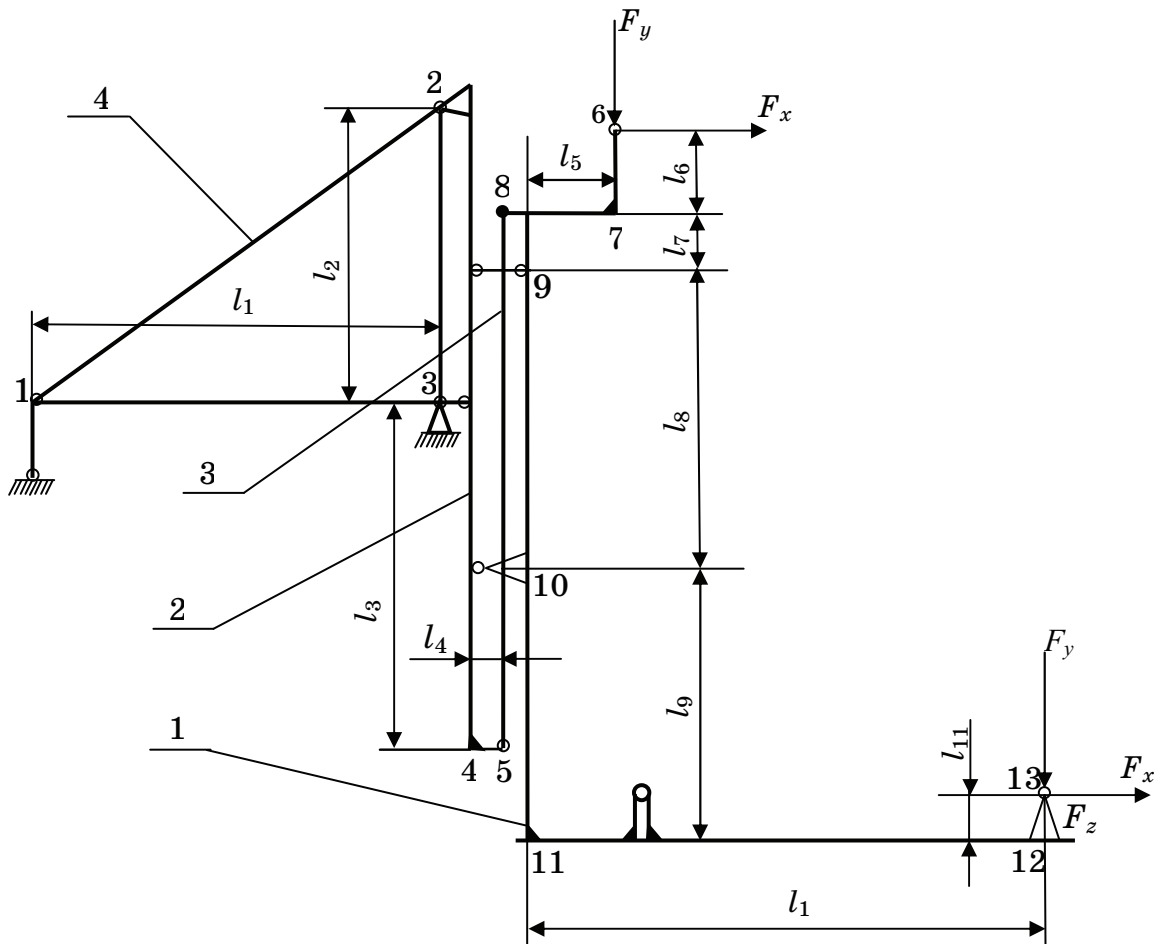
Розрахункова схема підйомно-зчеплювального пристрою
